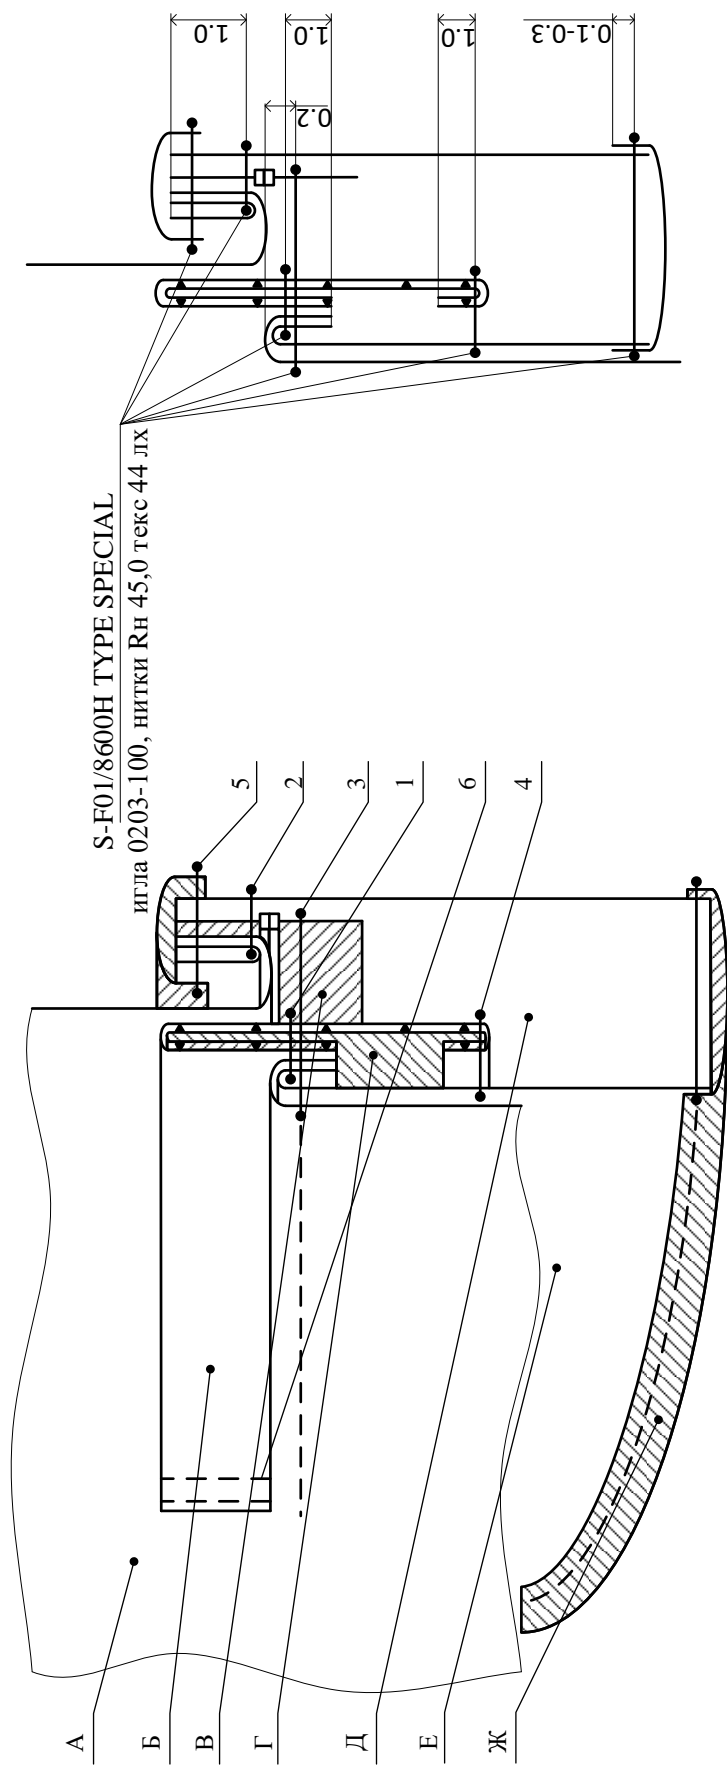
Схема обработки бокового прорезного кармана куртки костюма для сотрудников УИС
